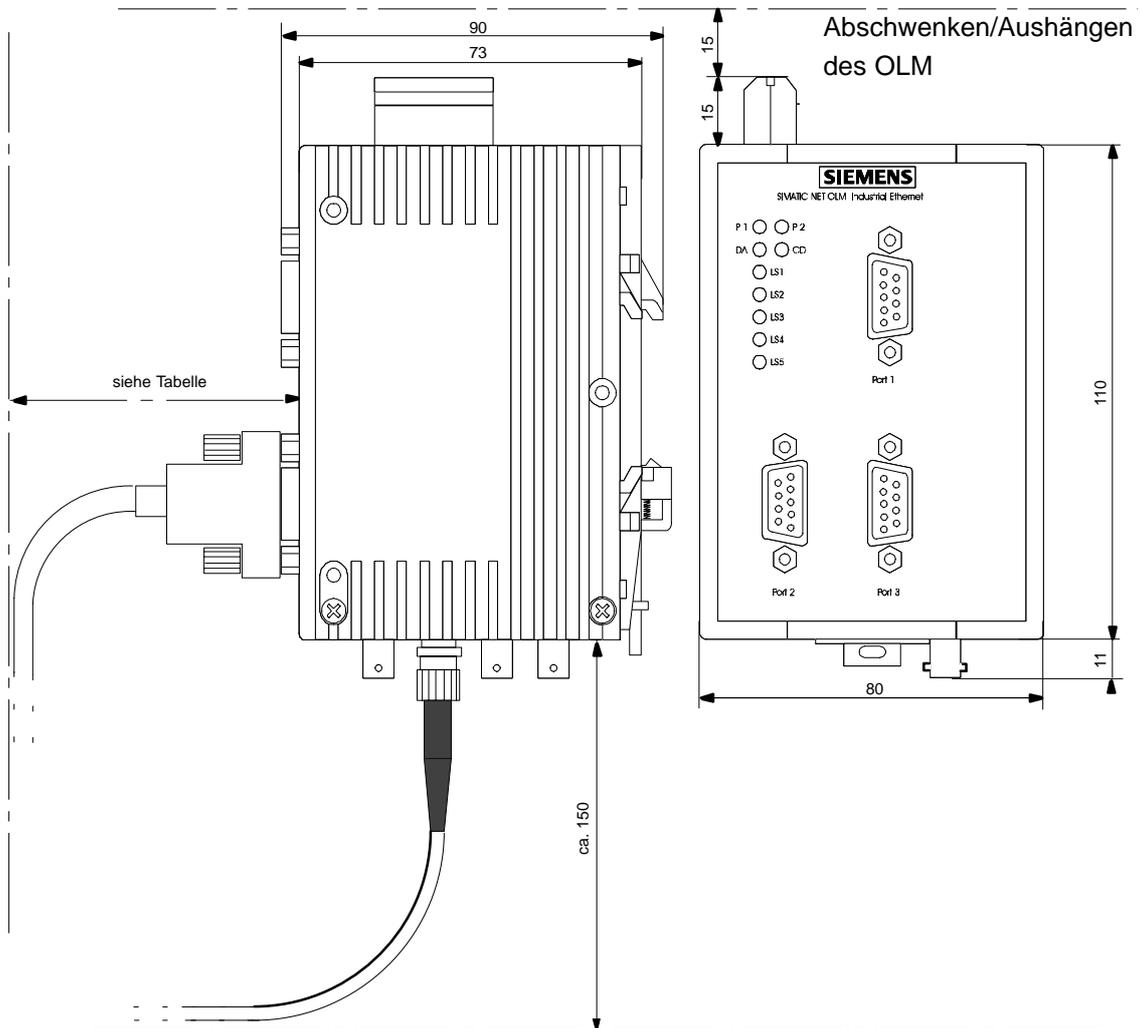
Industrial Ethernet OLM/ELM (Maße in mm)
